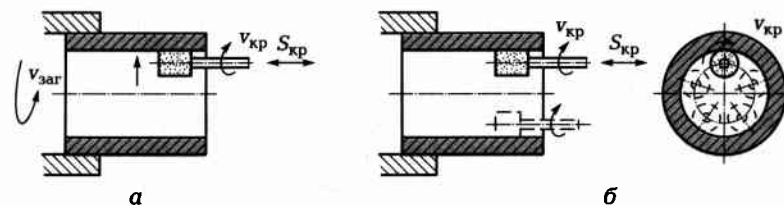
Схемы внутреннего шлифования отверстия во вращающейся (а) и в неподвижной (б) заготовках
